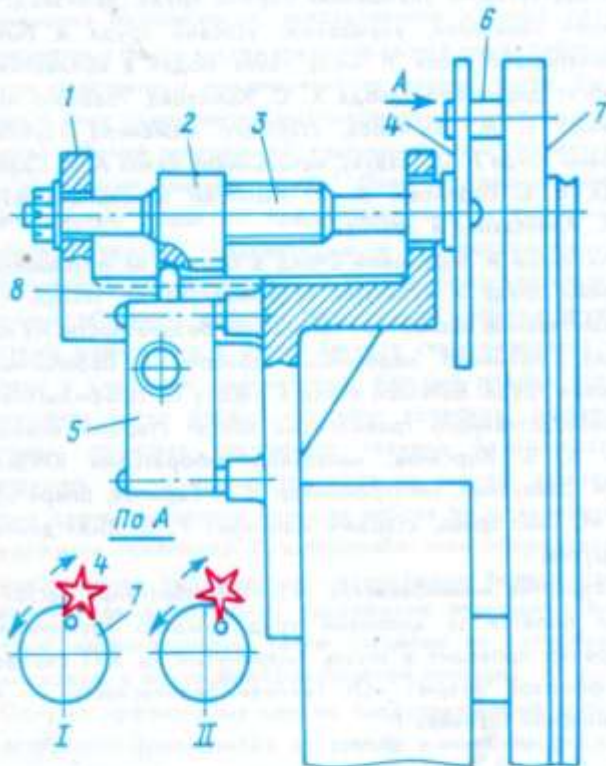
Старая конструкция ограничителя высоты подъема крюковой обоймы автомобильного крана: 1 — основание; 2 — гайка; 3 — винт; 4 — звездочка; 5 — конечный выключатель; 6 — ролик; 7 — барабан; 8 — шток конечного выключателя; I — нормальное вращение ролика и звездочки при их соприкосновении; II — изгиб лепестка звездочки при соприкосновении ролика и звездочки в упор
